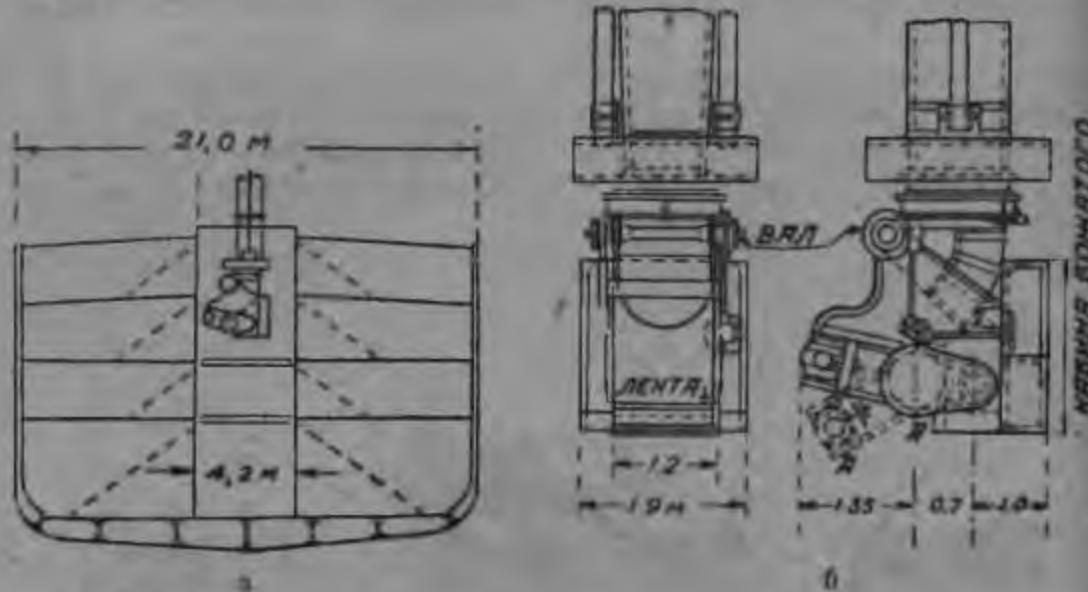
Правспособление (trimmer) для механической штазки угля в трюме.
